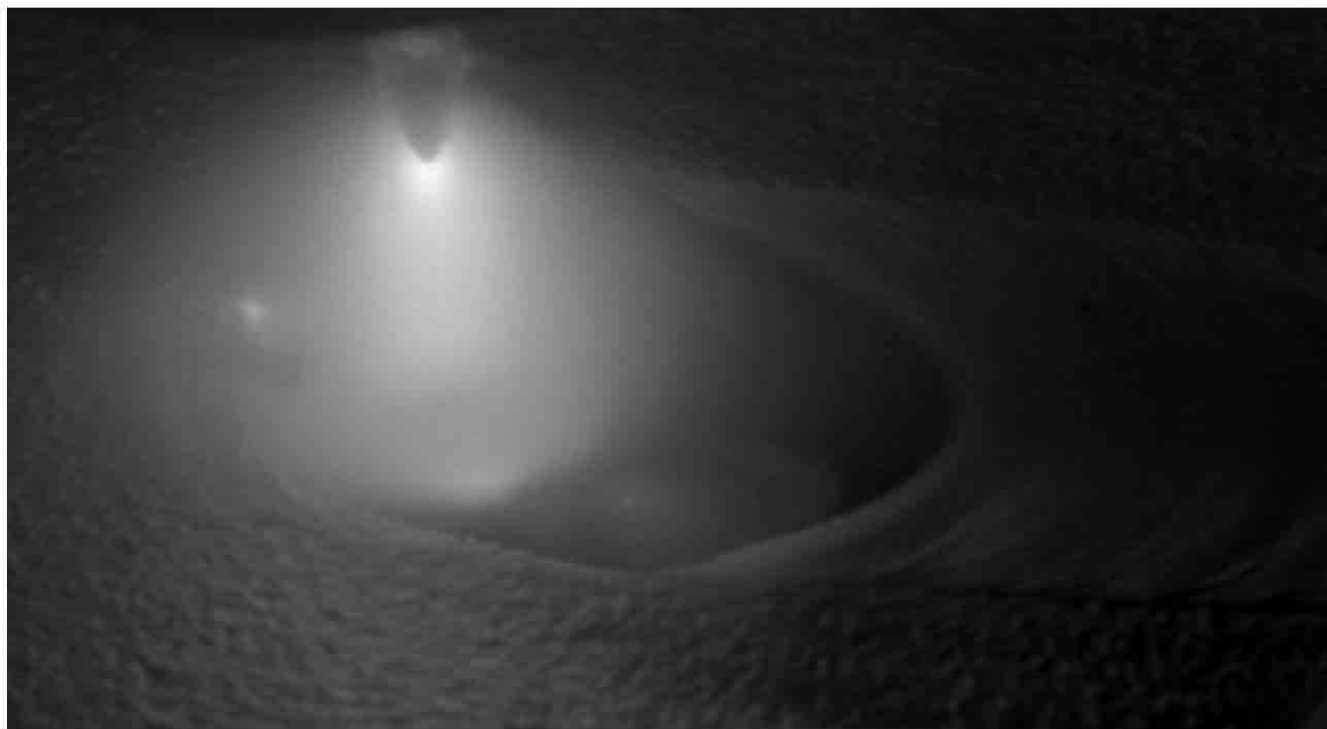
Класс GOOD WELD DEFF00 (процес якісного зварювання)
